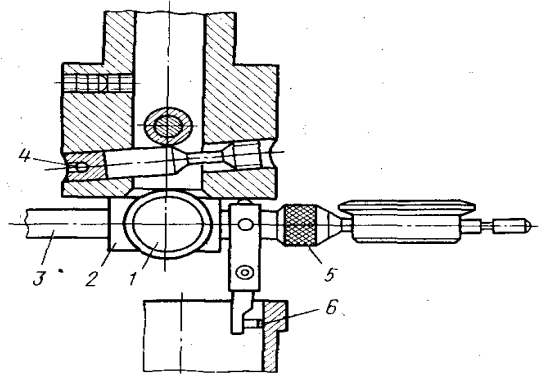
Резцовая головка станка 2А78Н с приспособлениями для центрирования гильз: 1 — винт; 2 — колодка; 3 — рычаг; 4 — шариковая оправка; 5 — гайка; 6 — упор рычага
